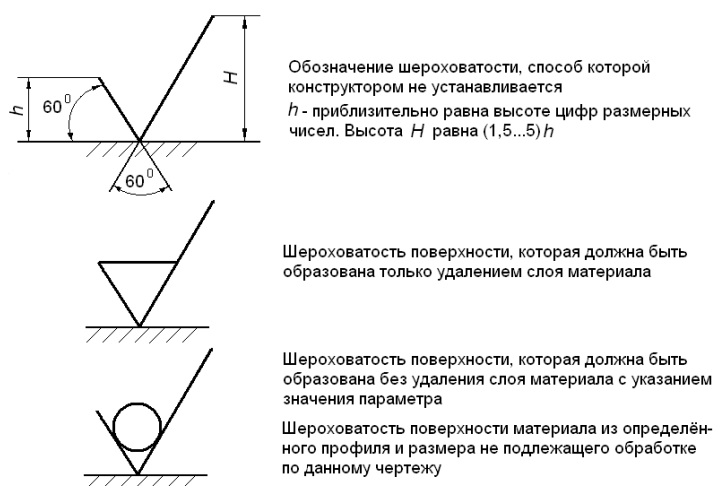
Обозначение на чертежах шероховатости поверхности
